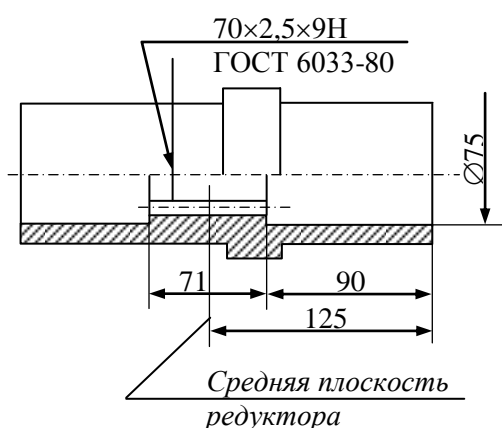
П7 Присоединительные размеры полого вала редуктора 1ЦЗУ-200
